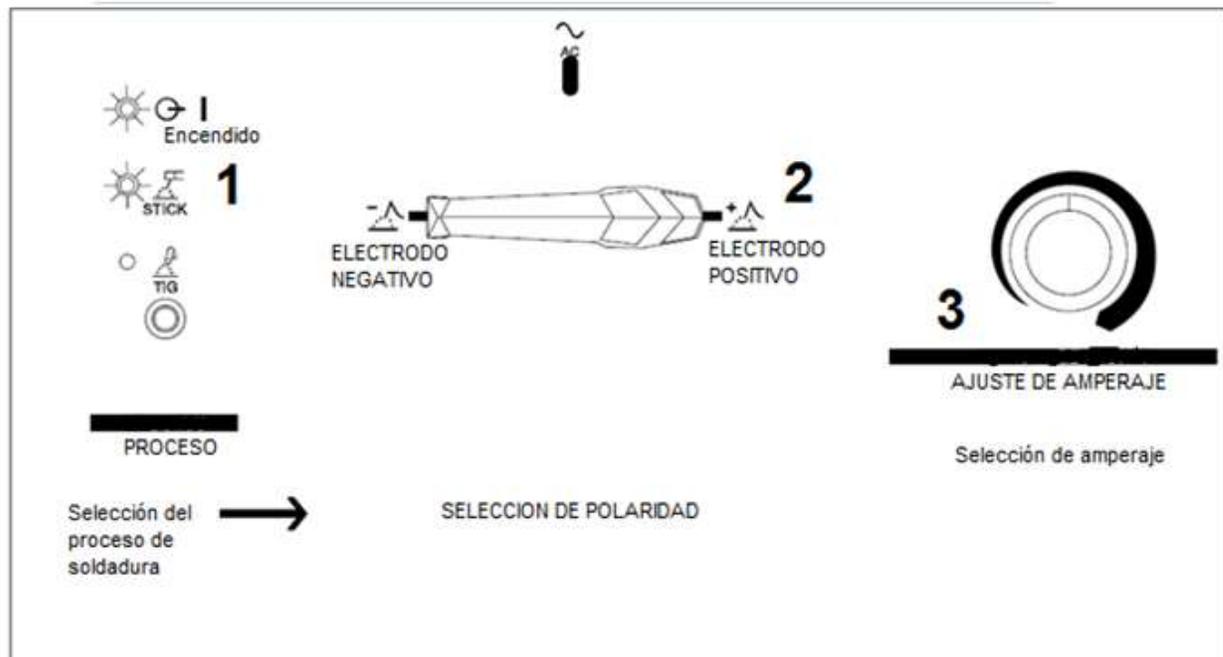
Pasos a seguir para soldadura con electrodo revestido
